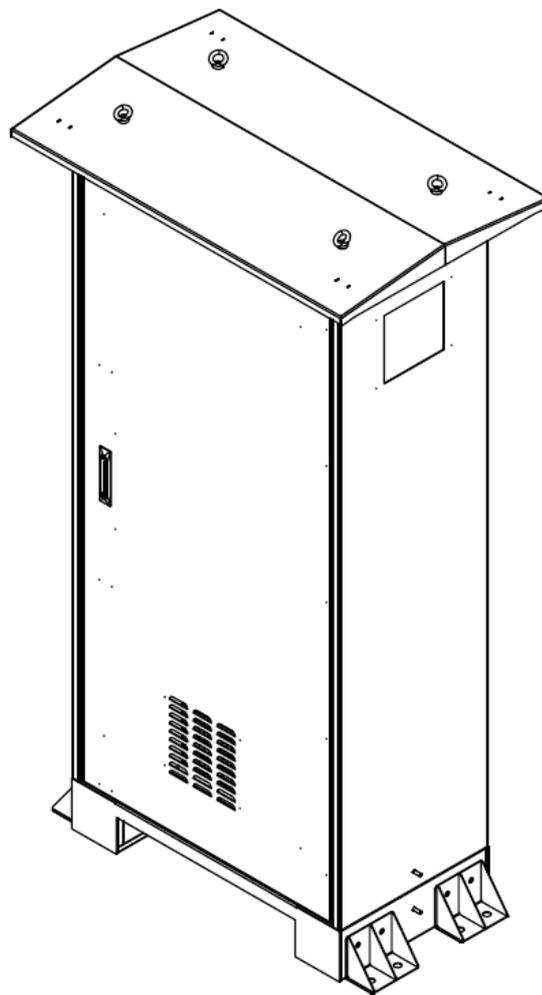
ТШВ-2195У2-Ех, общий вид шкафа.
